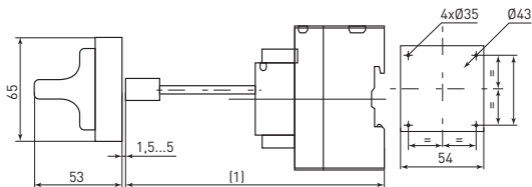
Габаритные размеры черной выносной рукоятки GV2
